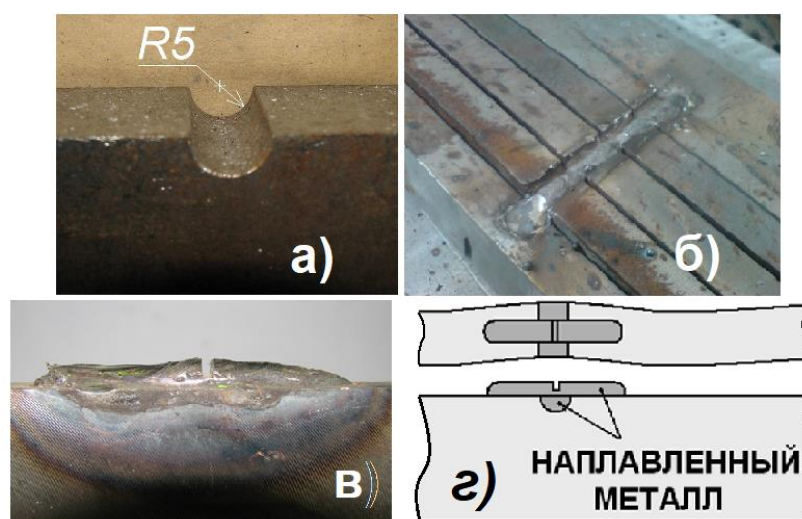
Нанесение хрупкой инициирующей наплавки с надрезом на образец ИППГ.
